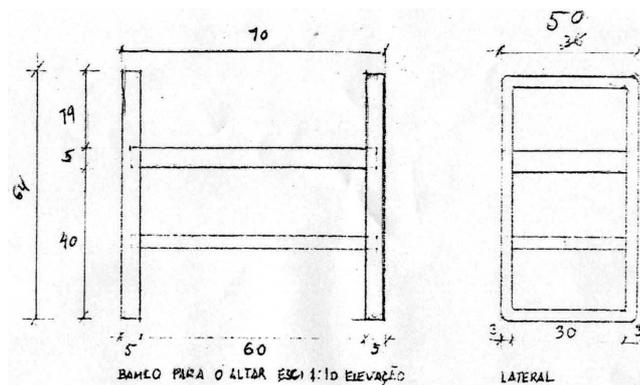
Banco para o Altar – [original desenhado em] Escala 1/10 – Elevação. Lateral. (Fonte: MNSG)
